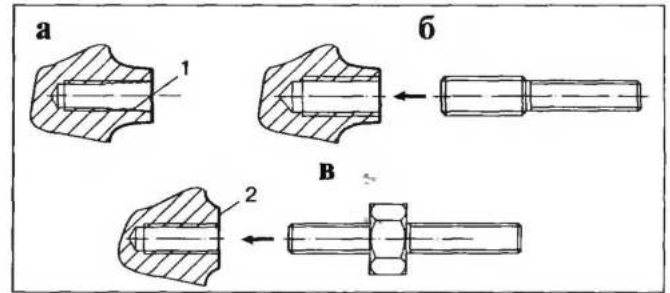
Некоторые способы ремонта резьбовых отверстий крепления деталей ГПМ:
